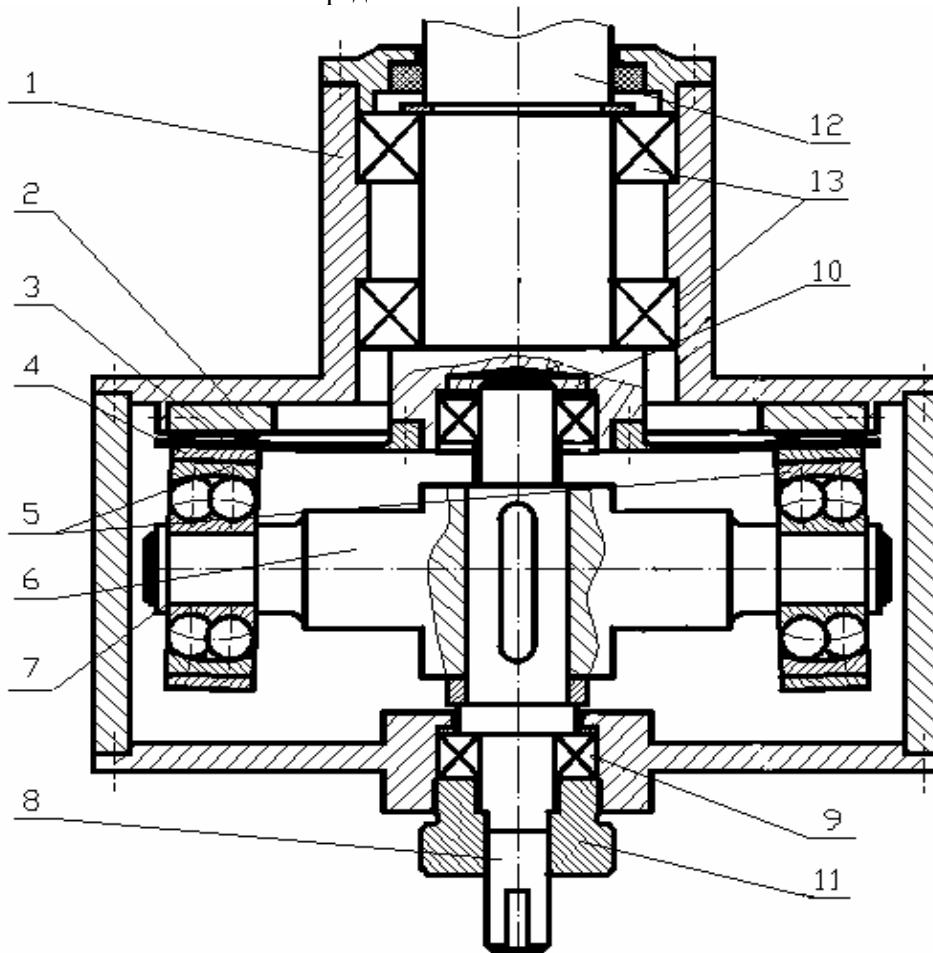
Конструктивная схема торцевой волновой зубчатой передача: 1 - корпус, 2 – жесткое колесо, 3 – гибкое колесо, 4 – подкладные втулки, 5 – сферические самоустанавливающиеся подшипники, 6 - генератор волн, 7 - стопорные шайбы, 8 – входной вал, 9 – подшипники, 10 – пружинные шайбы, 11 - регулирующая гайка, 12 – выходной вал, 13 – подшипники
